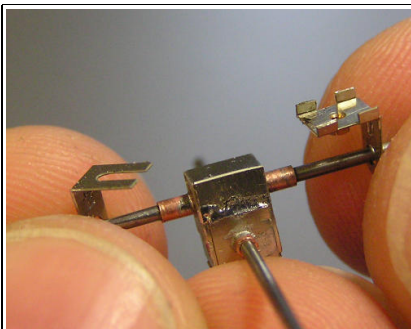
Die Achshalterungen so auf die Buchsen der Schneckenwelle stecken.
